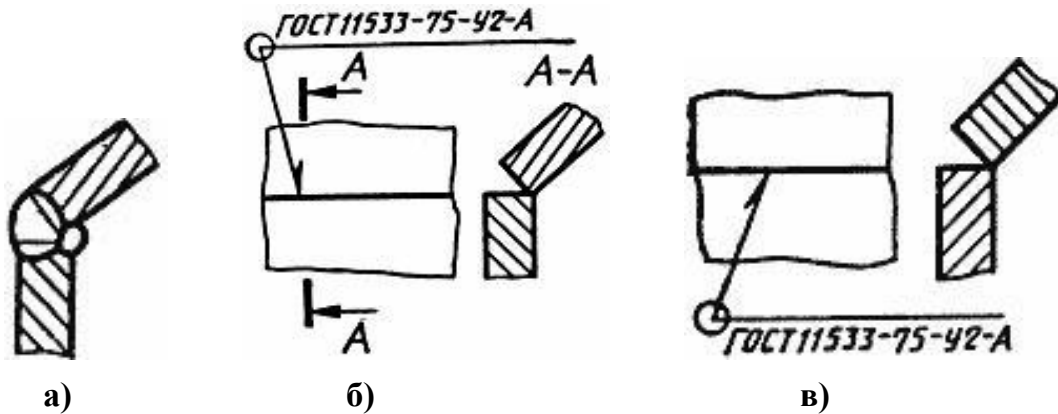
Пример обозначения сварного шва [5]: а – форма поперечного сечения шва; б – обозначение с лицевой стороны; в – обозначение с оборотной стороны
